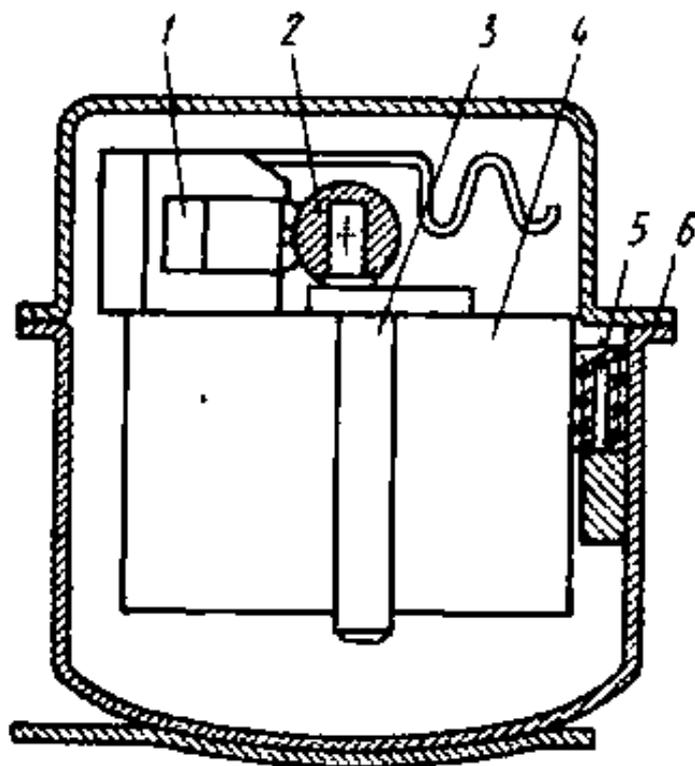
Компрессор ХКВ (ФГ) в сборе
